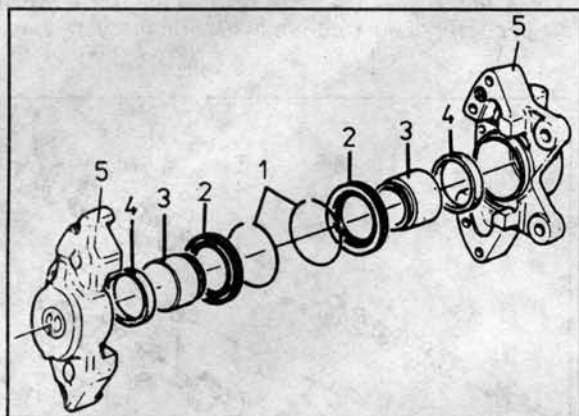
Способ посадки резиновых уплотнителей плунжеров тормозного цилиндра новой версии
